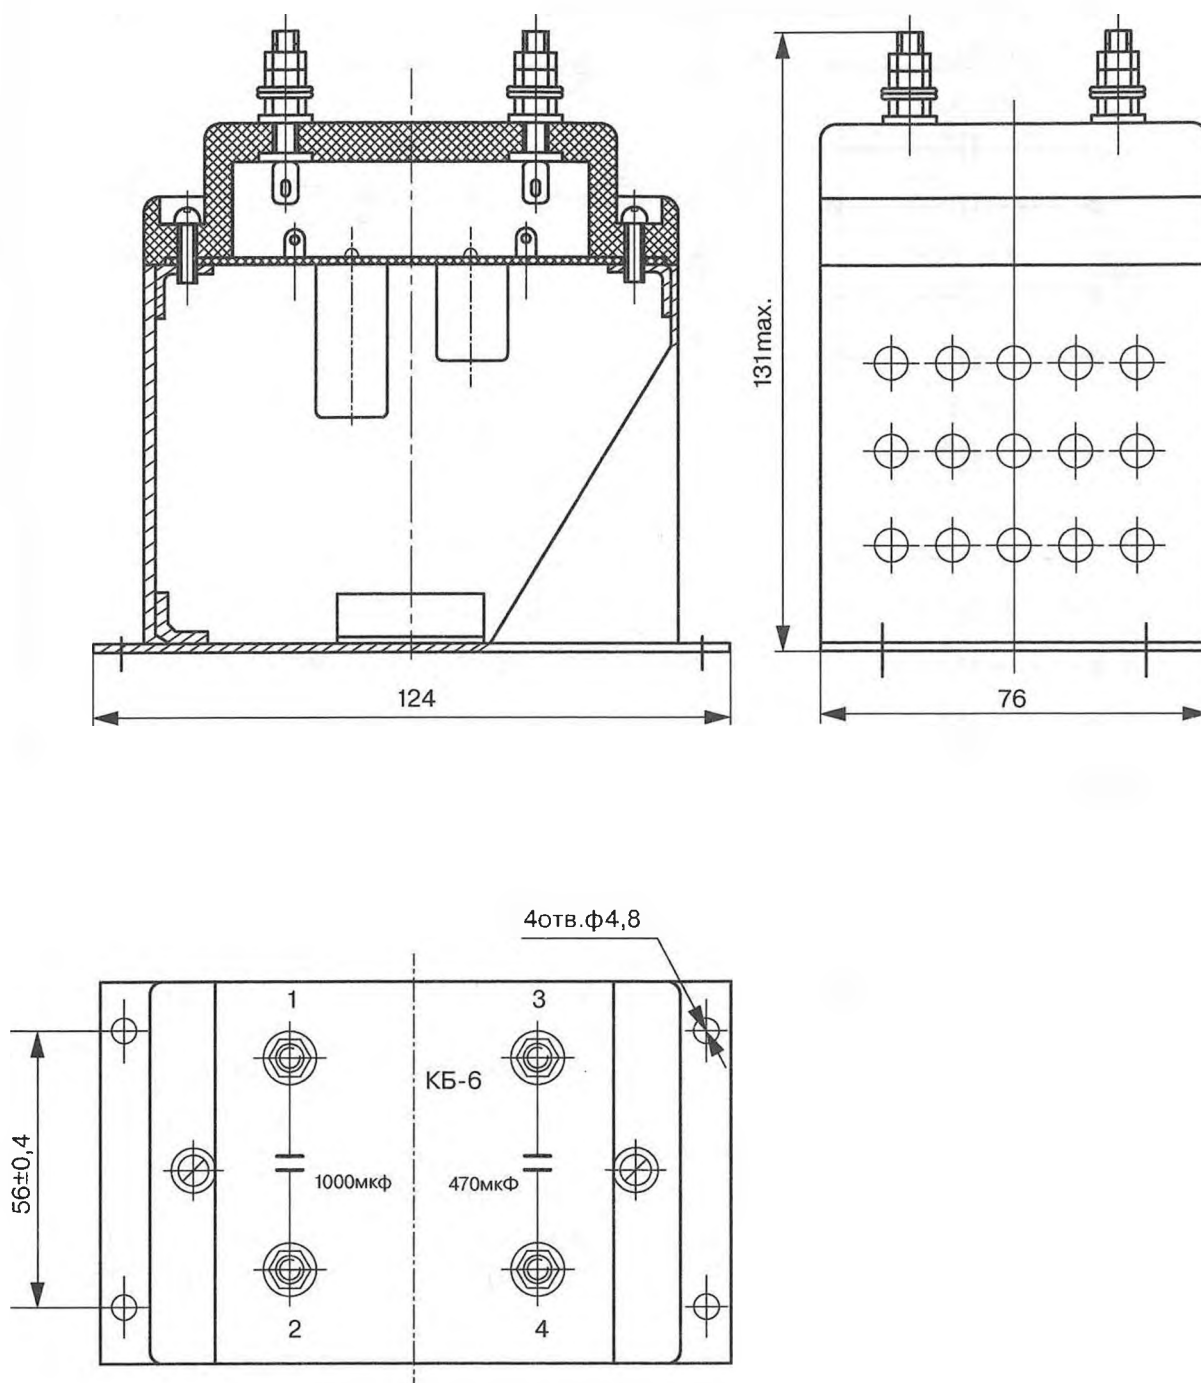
Габаритные и установочные размеры блока конденсаторного КБ-6
